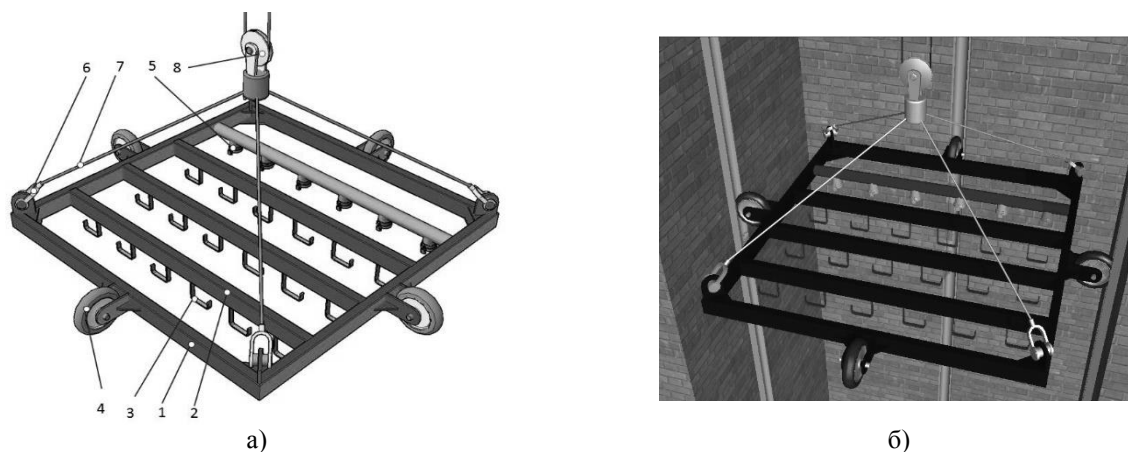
Конструкция устройства для подъема пожарных рукавов в башенную сушилку №1: а – проект конструкции подъемного устройства: 1 – рама; 2 – балка; 3 – крюк; 4 – колесо; 5 – патрубок с полугайкой; 6 – вертлюг; 7 – стропа; 8 – блок; б – визуализация устройства
